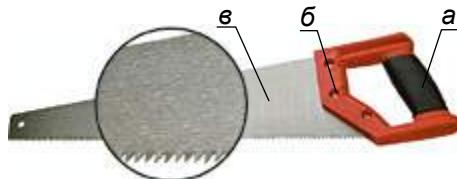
Строение ножовки: а – ручка; б – зажимные винты; в – металлическое полотно
